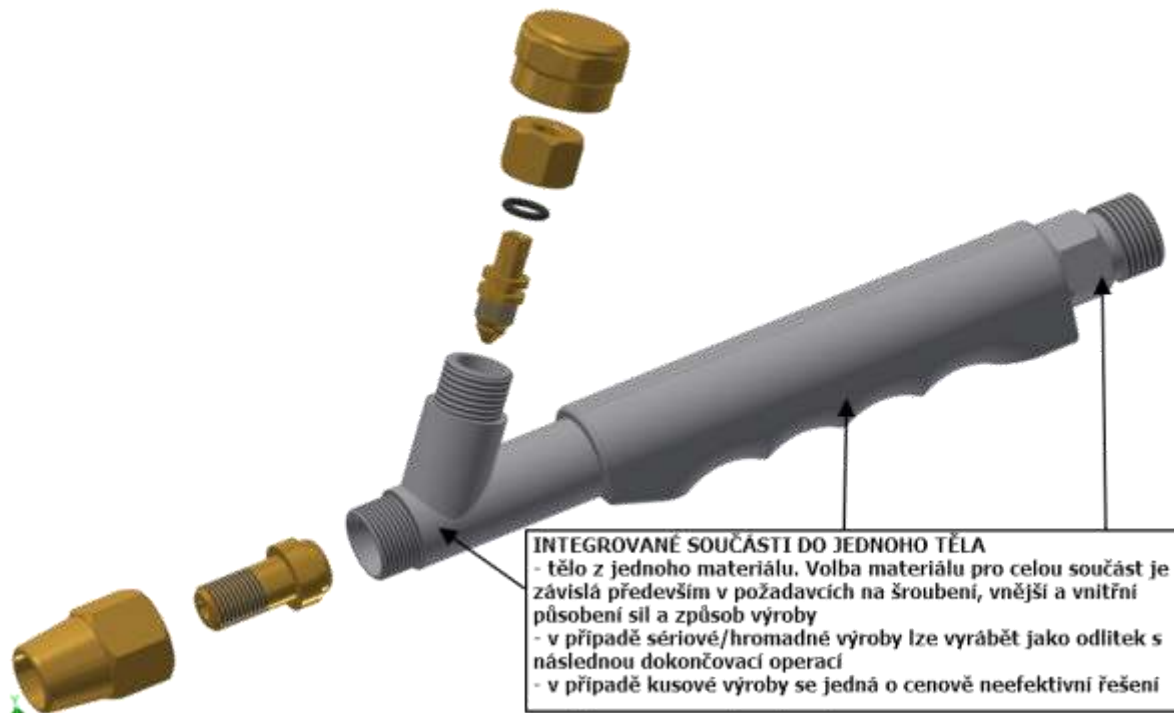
Stávající stavební struktura TS - plynový hořák [Sasiadek 2016]
